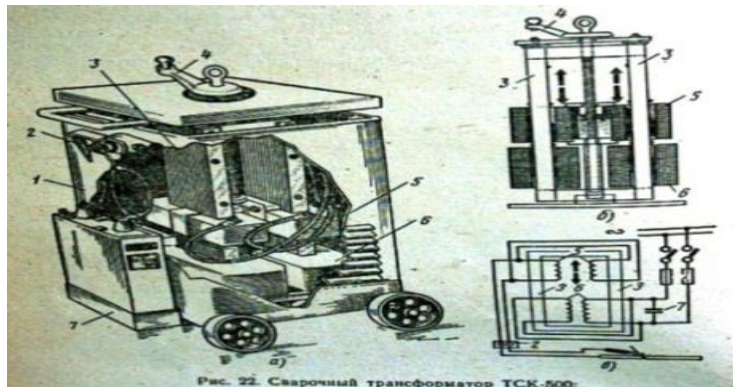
Сварочный трансформатор ТСК-500.
